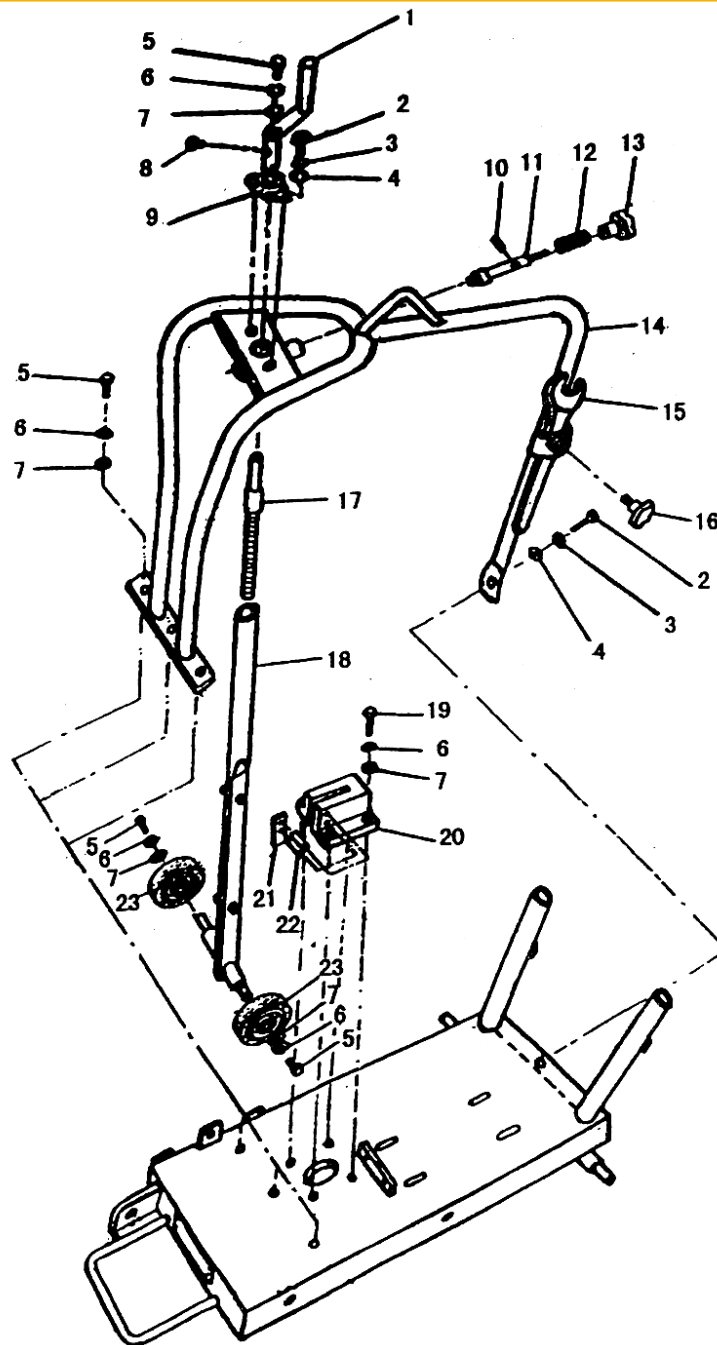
Ensemble de réglage de la profondeur de coupe
